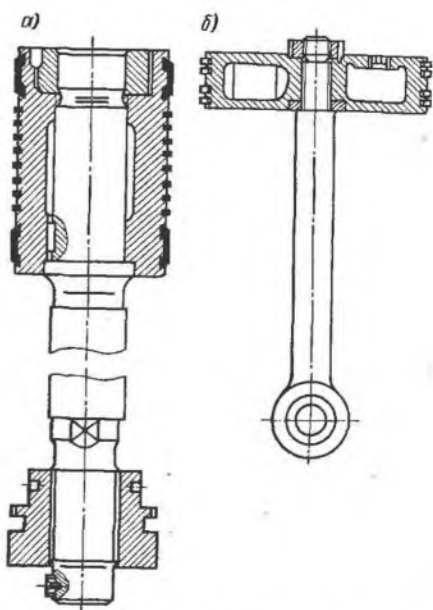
Конструкции штоков: а — с резьбовым соединением штока с крейцкопфом; б — с шарнирным соединением штока с крейцкопфом
